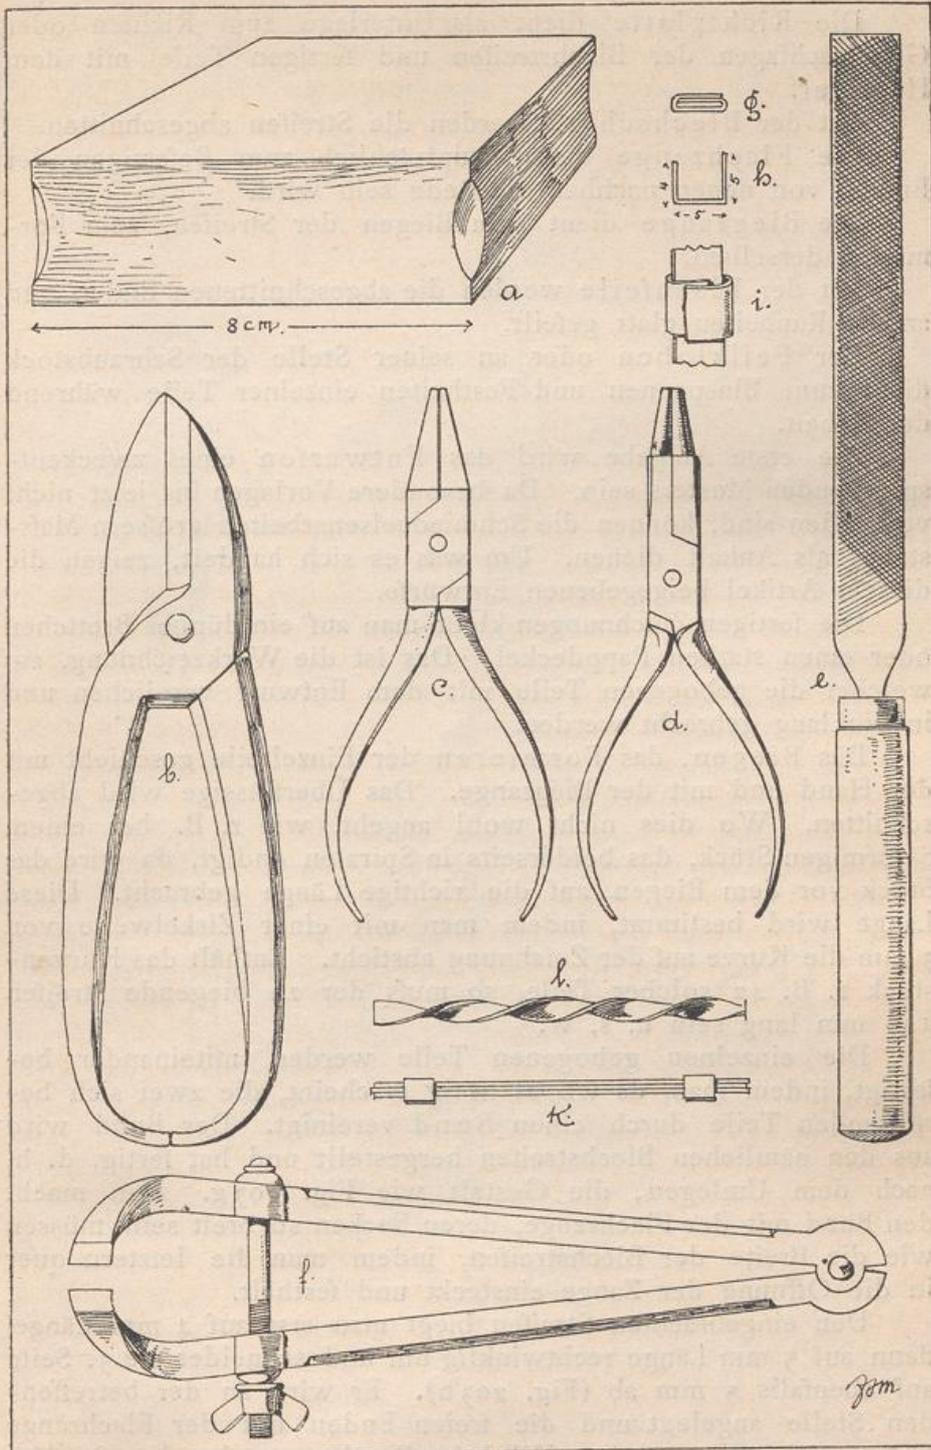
Werkzeuge für die Klein-Eisen-Arbeit.
